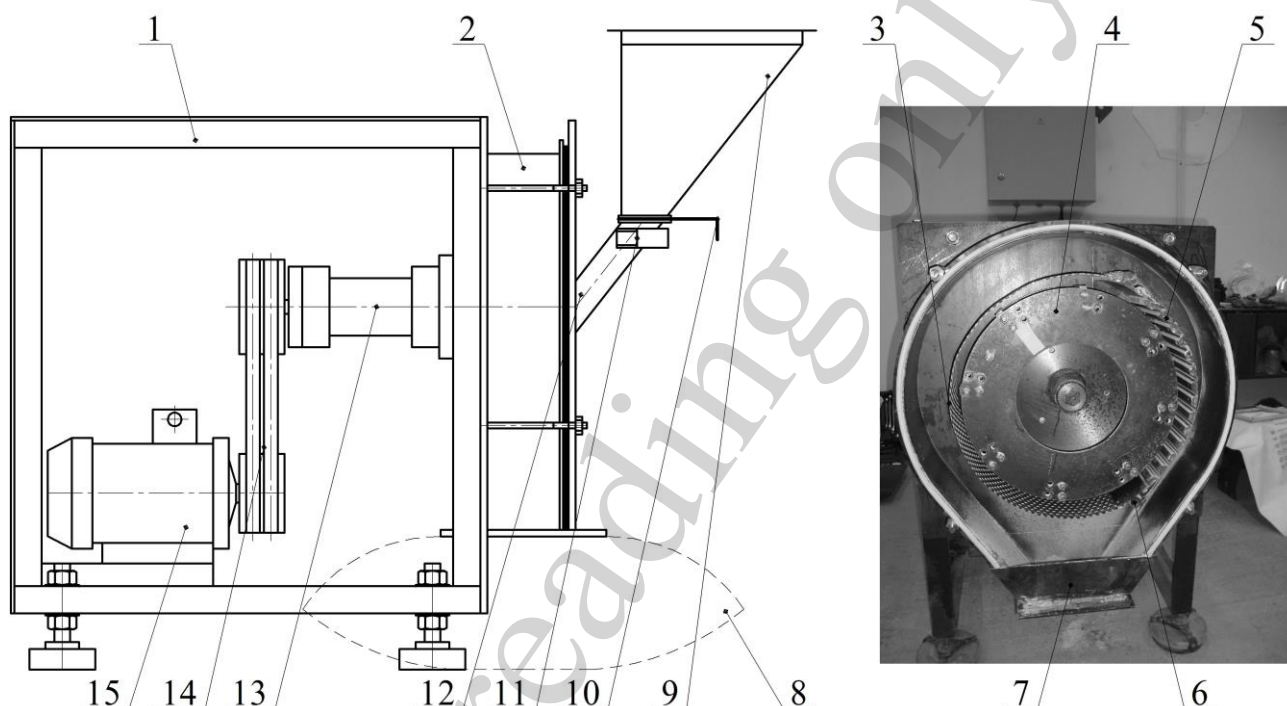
Измельчитель фуражного зерна: 1 – станина; 2 – камера рабочая; 3 – решето; 4 – ротор; 5 – дека; 6 – кронштейн; 7 – горловина выгрузная; 8 – фильтр-мешок; 9 – бункер; 10 – заслонка регулировочная; 11 – отверстие с шиберной задвижкой; 12 – горловина загрузочная; 13 – корпус подшипников; 14 – передача клиноременная; 15 – электродвигатель
